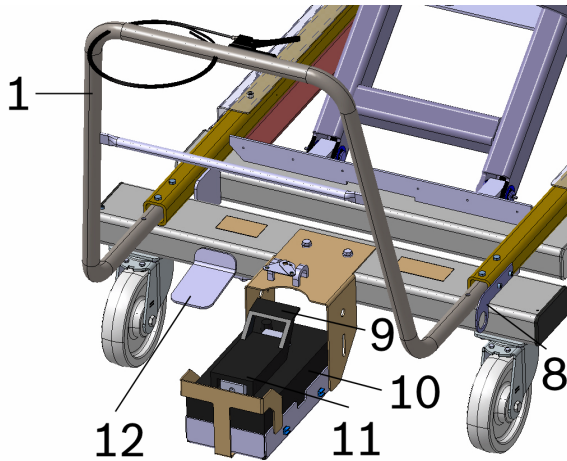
Collegamento del tubo flessibile dell'aria compressa al piano elevatore a pantografo
